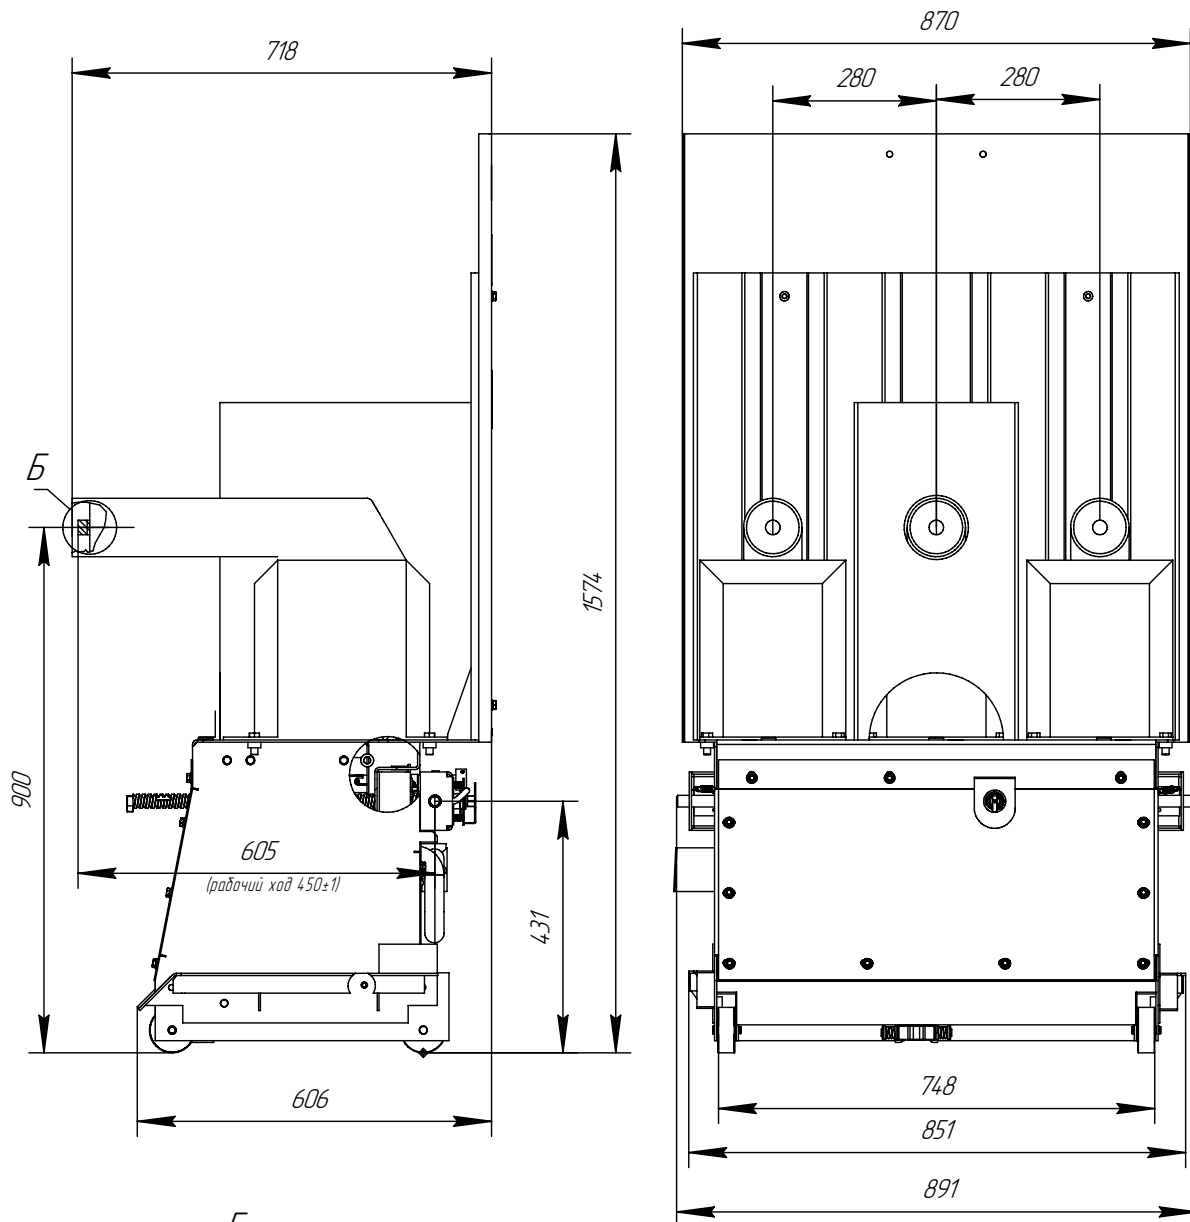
Габаритно-установочные и присоединительные размеры выключателей серии ВР35.
